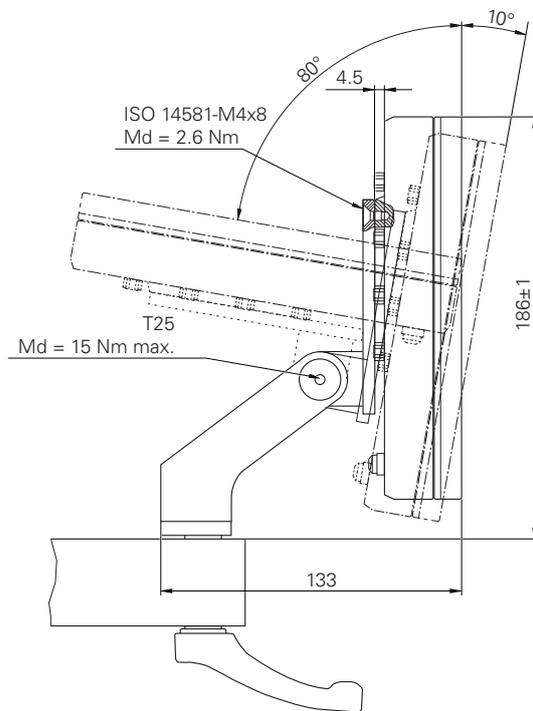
Dimensiones del aparato con soporte Multi-Pos
